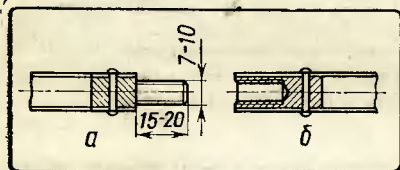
Подготовка лыжных палок для сборки лавинного щупа:
